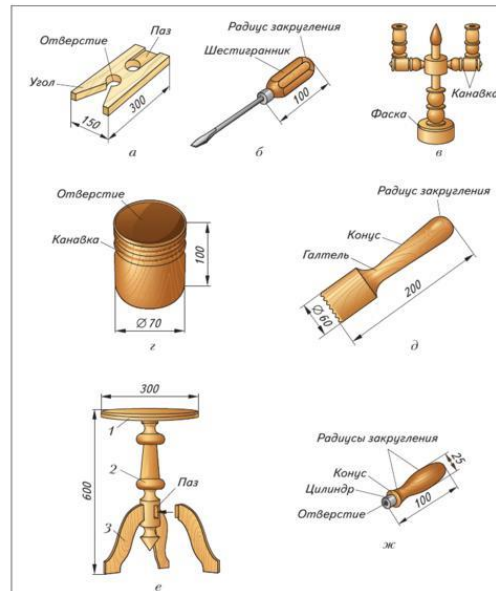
Изделия из древесины и их конструктивные элементы: а — выпиловочный столик; б — отверстие; в — подстелочник; г — стаканчик для ручек и карандашей; д — толкушка; е — столик; ж — ручка папируса
